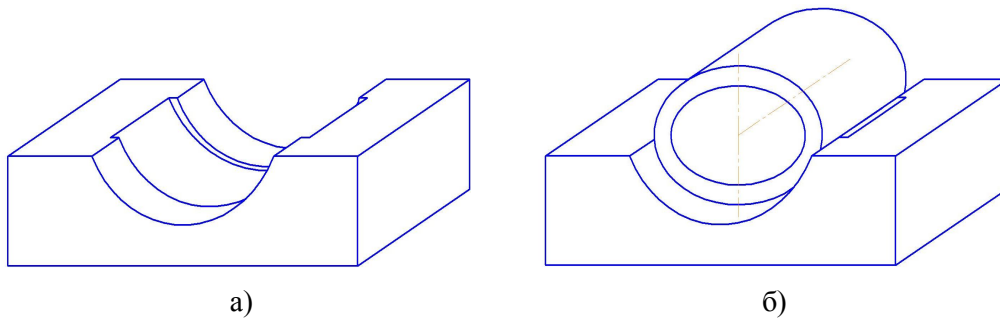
Применение шаблона для восстановления опорной поверхности подшипника: а – выработанное место опорной поверхности подшипника; б – шаблон установлен, излишки материала композита выдавлены на плоскость разъема
